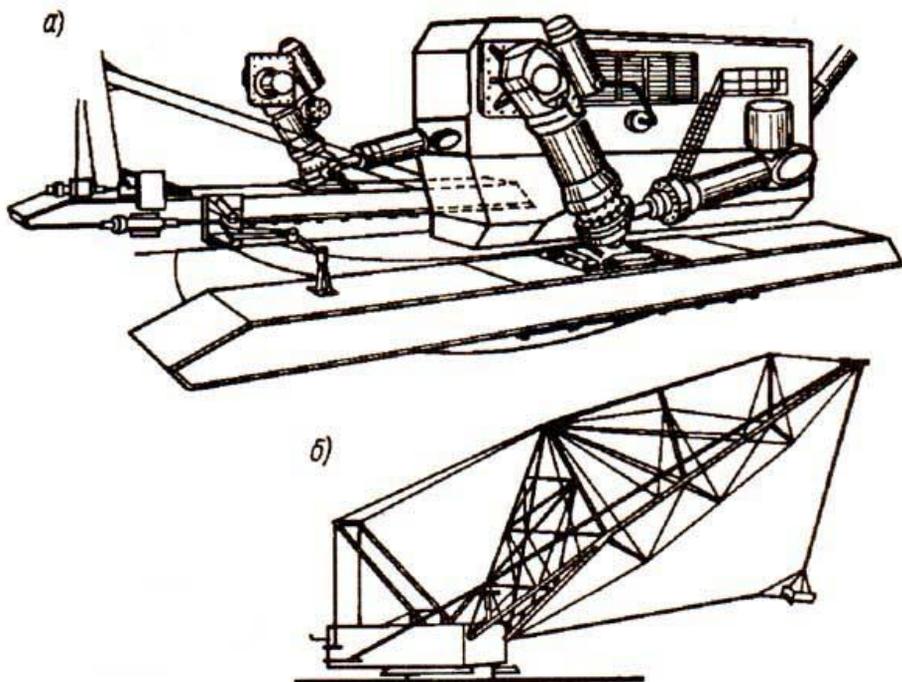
Схема: а – шагающего механизма, б – шагающего экскаватора
